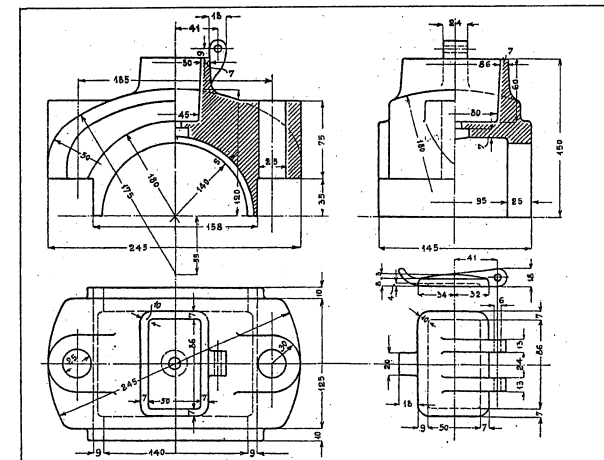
/4: Lagerdeckel mit Verschlussdeckel (um 1900)
